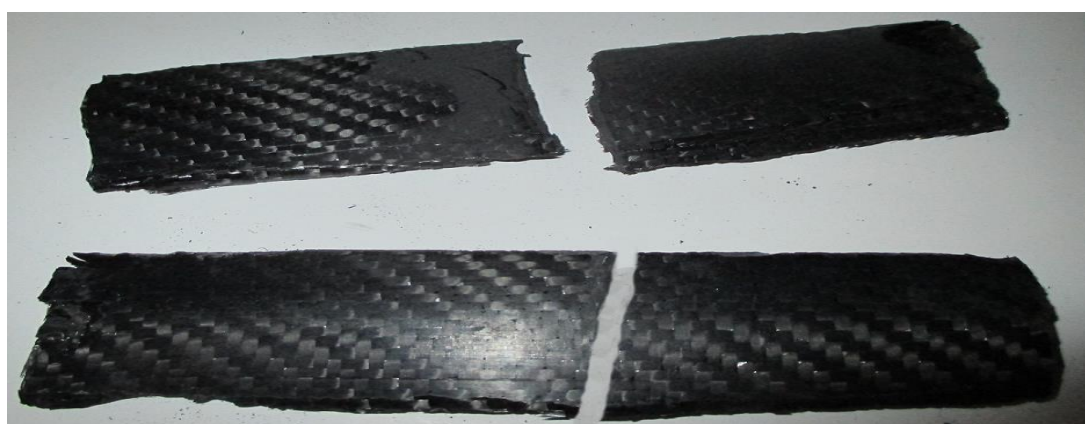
Zkušební vzorky č. 3 a 5 pro Impact test
